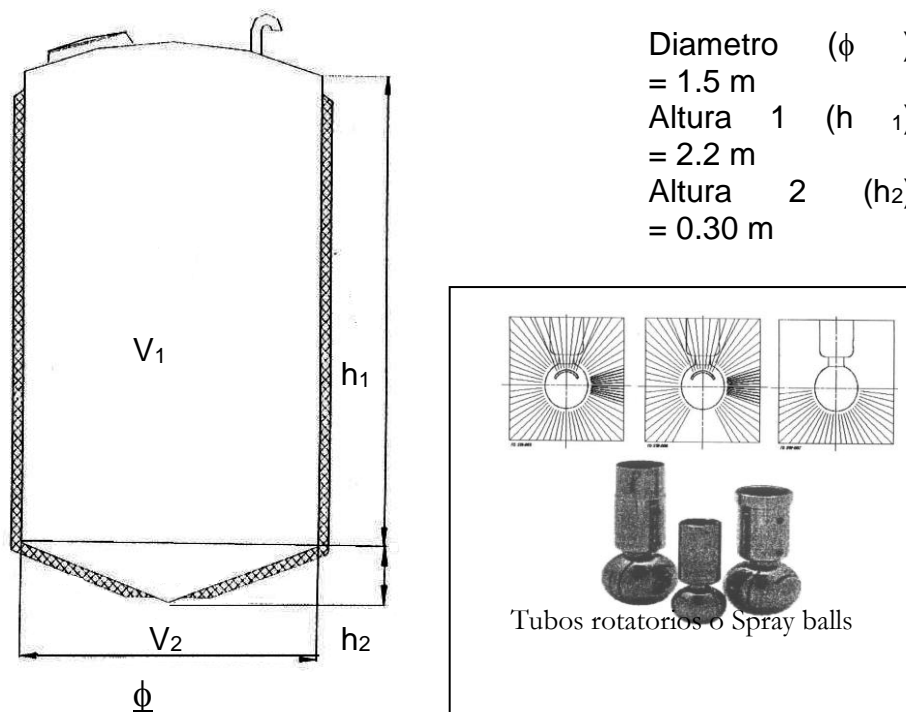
TANQUE CIP CON SPRAY BALL O TUBOS ROTATORIOS
